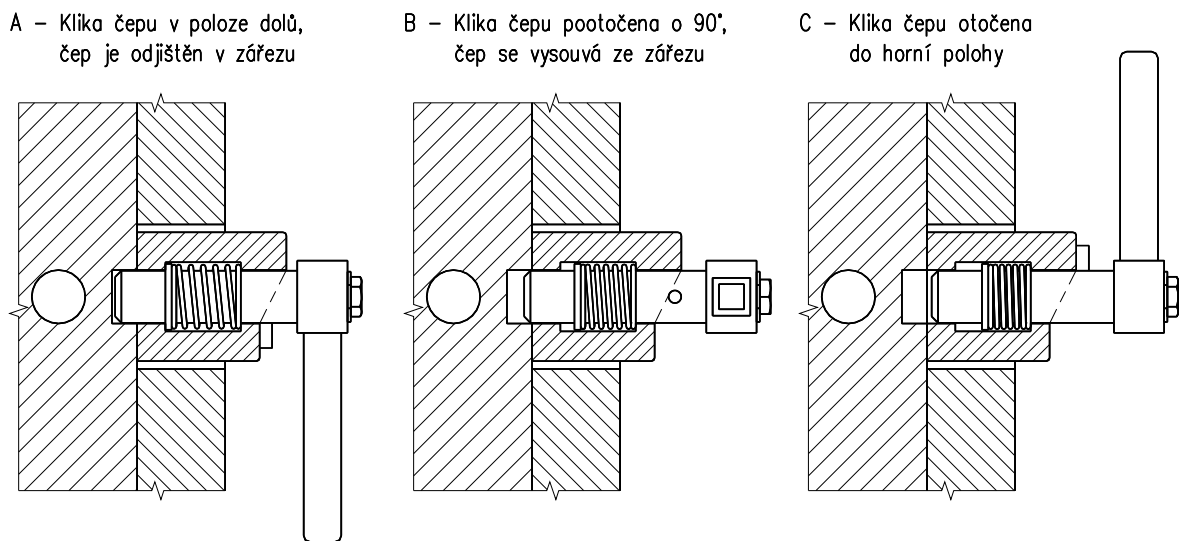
Příklad řešení soustavy zajišťovacího čepu s klikou
